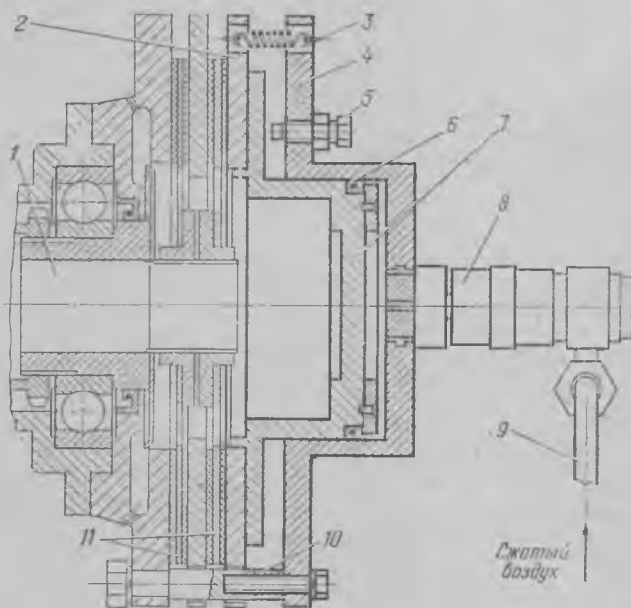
Фрикционная муфта (модернизированная): 1 — вал редуктора; 2 — прижимной диск; 3 — фиксатор с пружиной; 4 — воздушный цилиндр; 5 — упорный винт; 6 — манжета; 7 — нажимной поршень; 8 — воздухоподводящий штуцер; 9 — шланг; 10 — втулка; 11 — фрикционные диски
